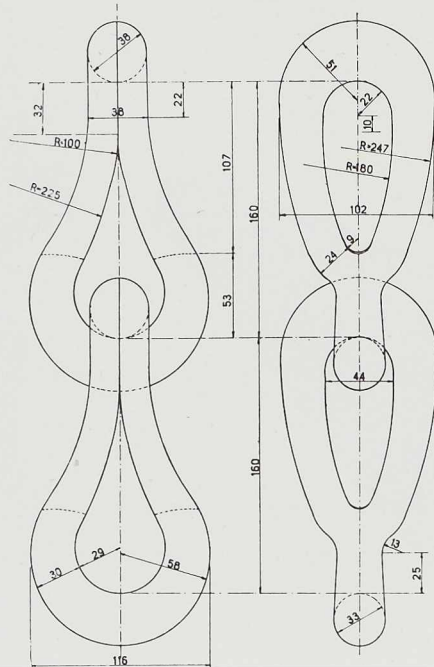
Maillons pour chaînes sans soudure en acier (1920).
